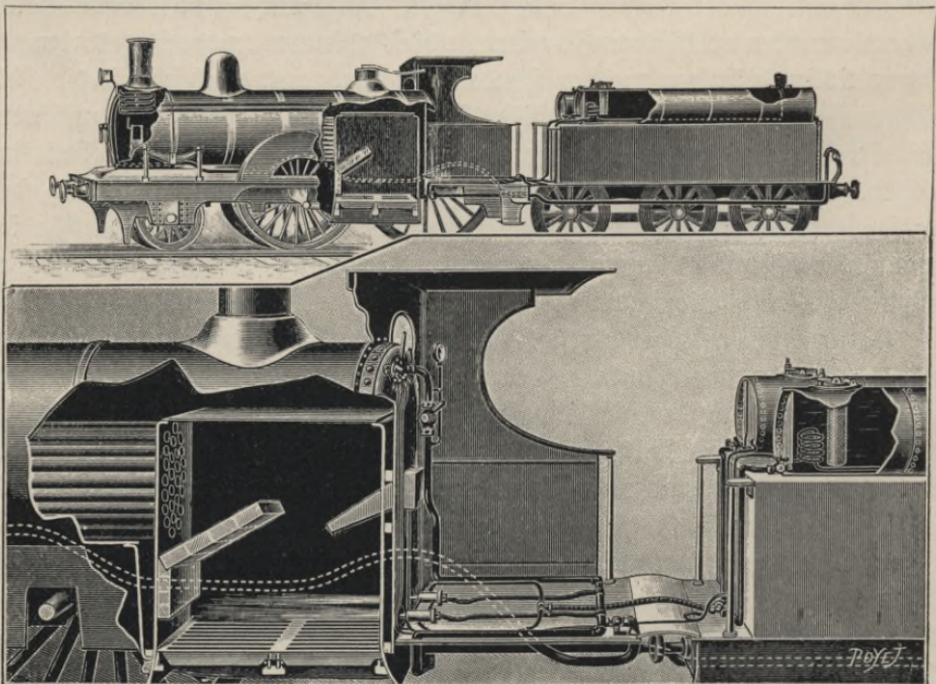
Einrichtung einer Lokomotive für Ölfeuerung.
